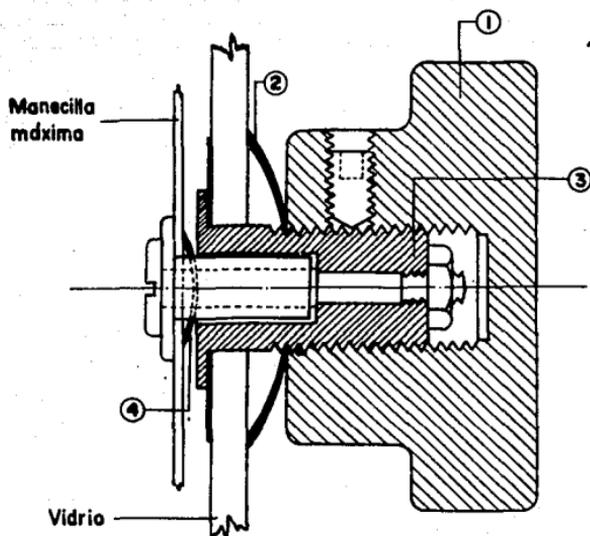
Sección de lado a lado del ensamble de la manecilla máxima
